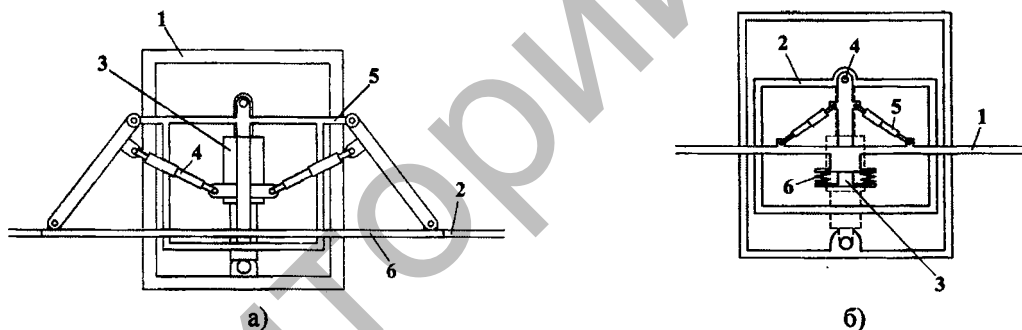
Штанги опрыскивателей с демпфирующими устройствами
